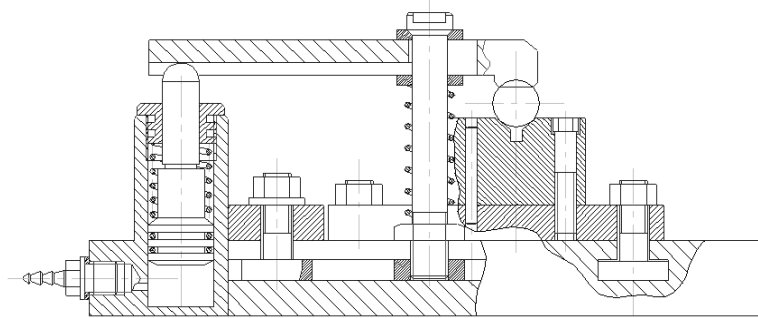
Пристрій для фрезерування пазів у втулці
